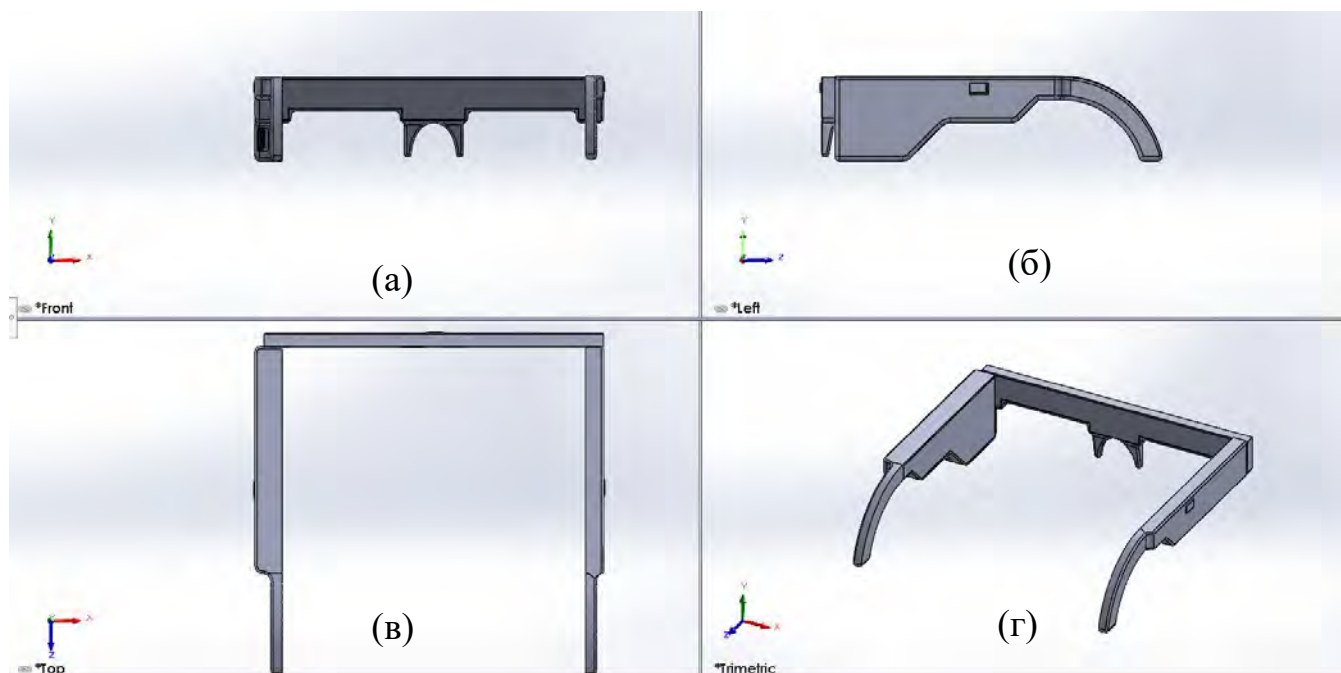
Збірка корпусу: а) вигляд ззаду; б) вигляд зліва; в) вид зверху; г) ізометричний вигляд
